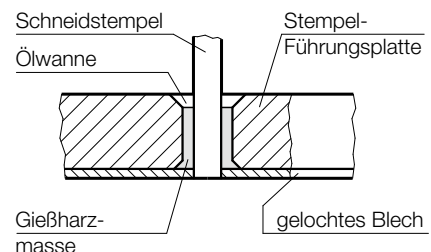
Vergossener Schneidstempel für schnellaufende Werkzeuge.
